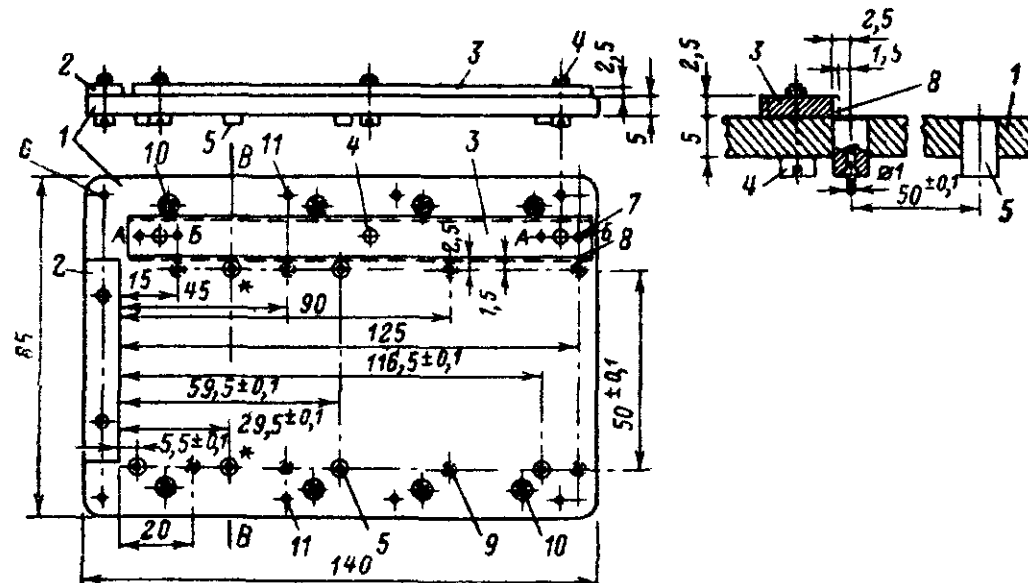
Кондуктор для сверления отверстий под фиксирующие штифты в платах.
